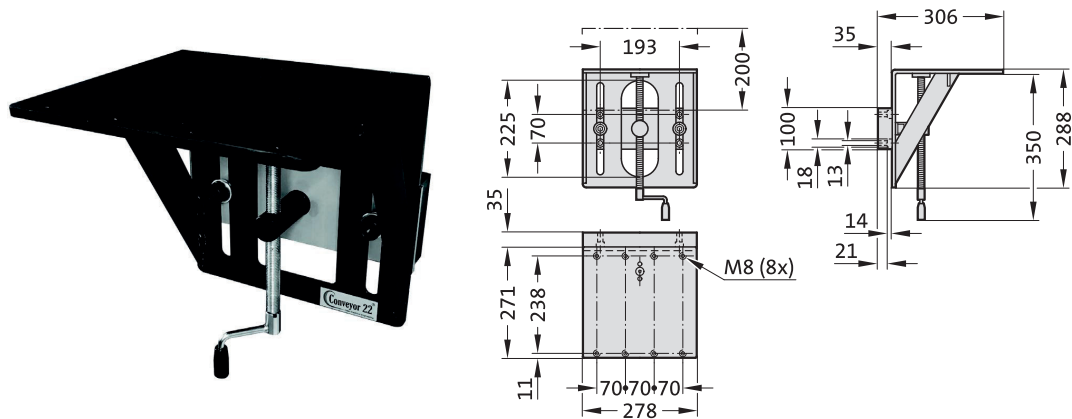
Angle de montage réglable en hauteur pour le montage du transporteur
